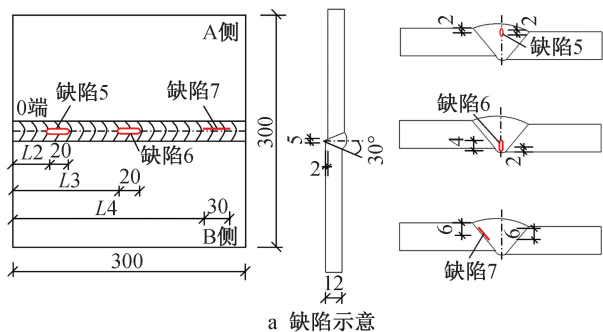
试件 JMHS-221225 焊缝缺陷设置
